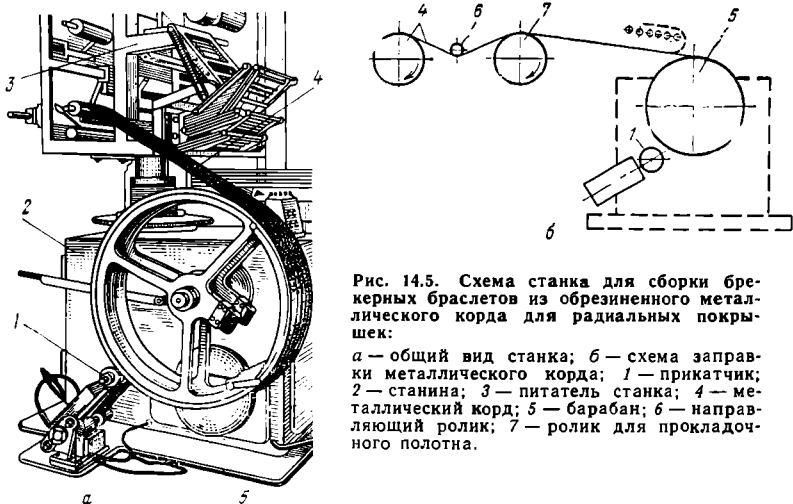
Схема станка для сборки брекерных браслетов из обрезиненного металлического корда для радиальных покрышек:
